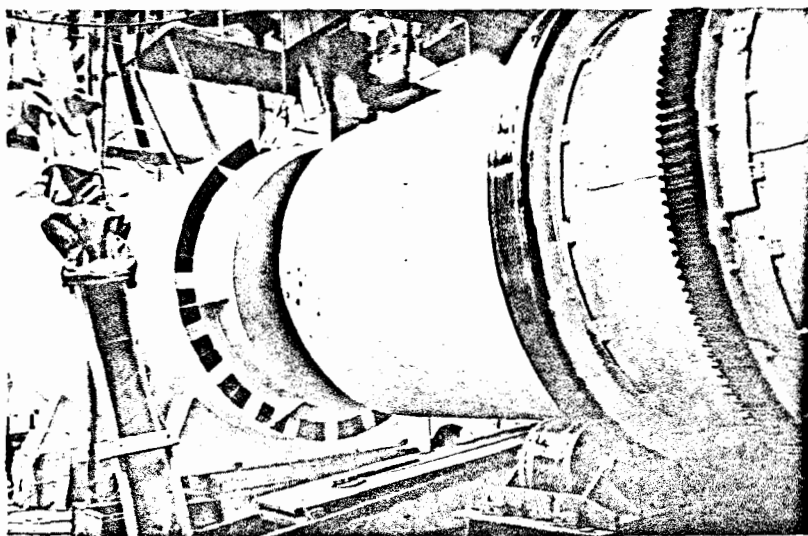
Horno rotativo para producir 5,0 toneladas/hora de harina de pescado. Nótese la estructura de apoyo, los rodamientos y engranajes impulsador.
